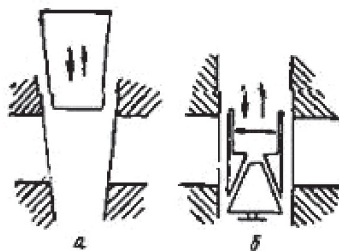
Способы уплотнения шиберов: а — клиновой; б — параллельный
